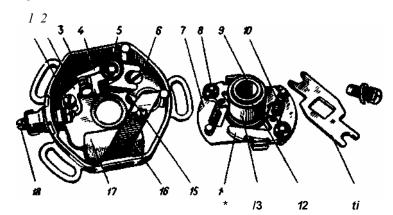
Прерыватель ПМ302A с автоматом опережения зажигания: I - винт; 2 \*• контактная стойка, 3 - корпус прерывателя, 4 - рычаг прерывателя; 5 - ось рычага; 6 - эксцентрик; 7 - автомат опережения зажигания; 8 - ось грузика; 9 - втулка; 10 - пружина; 11 -поводок; 12 - кольцо запорное; 13-кулачок; 14-грузик; 15-фильц; 16 - держатель конденсатора; 17 - конденсатор; 18 - клемма
